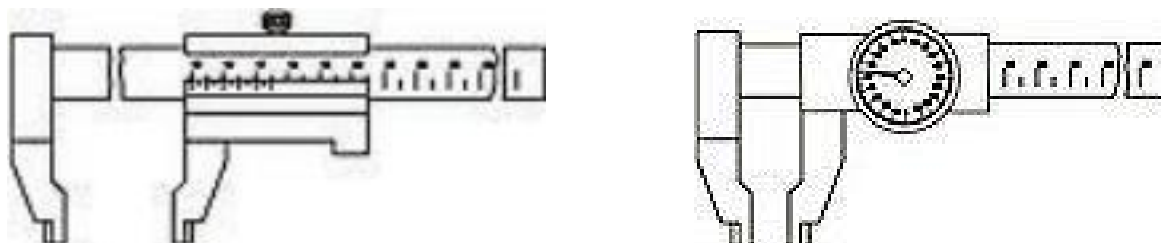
Штангенциркуль ШЦ-III-125-0,05 [ДСТУ 166-86]
